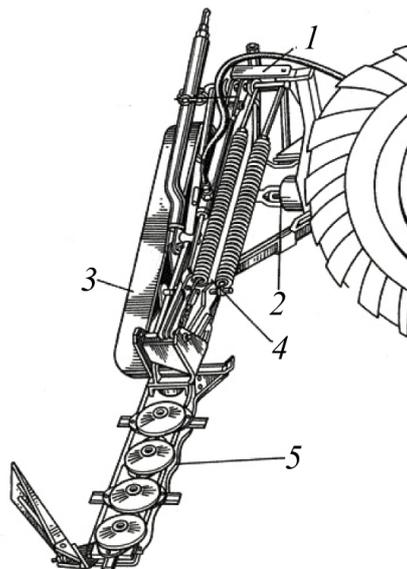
Косилка АС-1: 1 – навеска; 2 – ВОМ; 3 – защитный кожух ремня; 4 – пружинный блок; 5 – режущий аппарат
